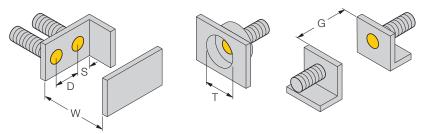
Minimale Montageabstände – Zylinderbauformen, bündig einbaubar
